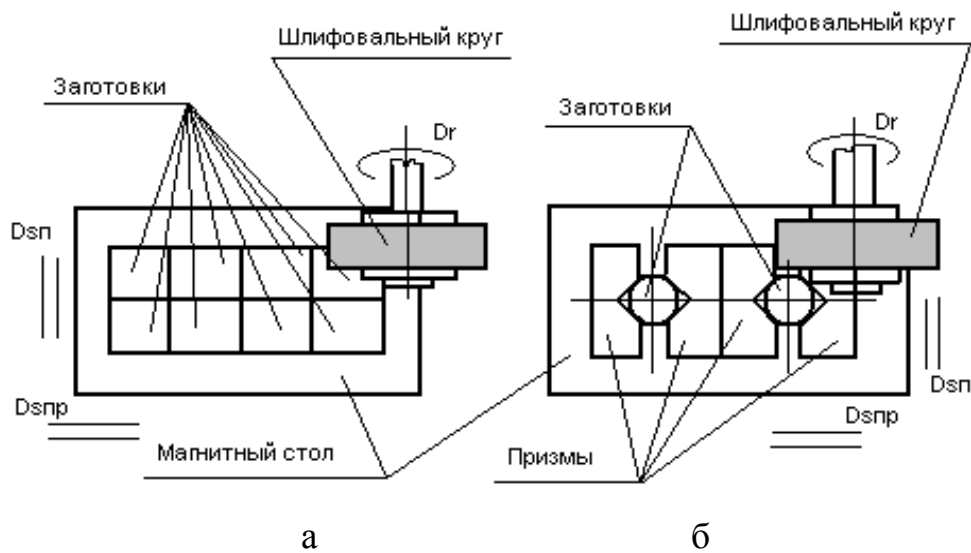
Схемы установки при многоместной обработке: а – на магнитной плите, б – с помощью специальных приспособлений (призм)
